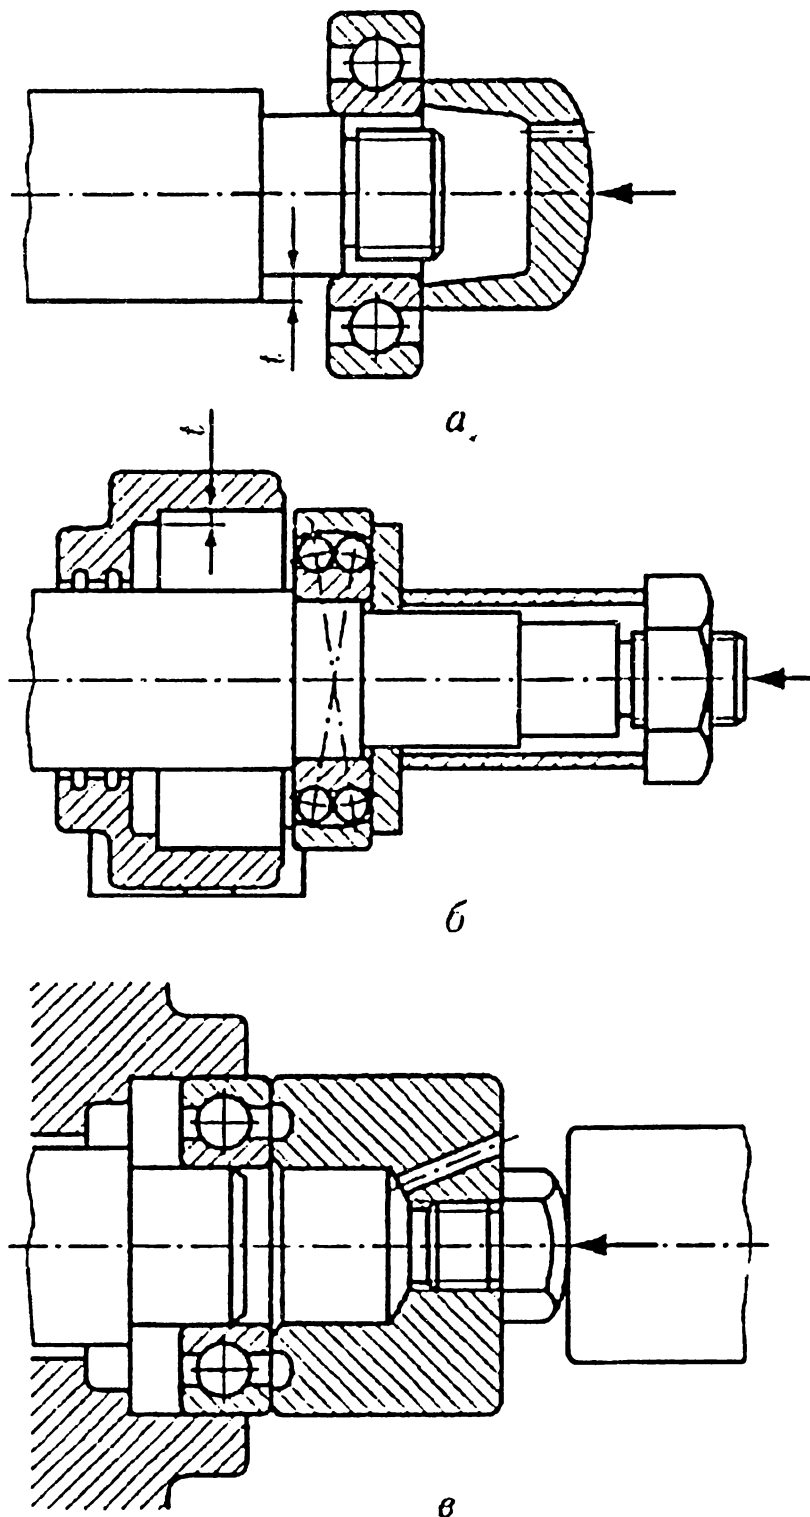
Способы монтажа подшипников на вал (а), в корпус (б) и одновременно на вал и в корпус (в) [1]
